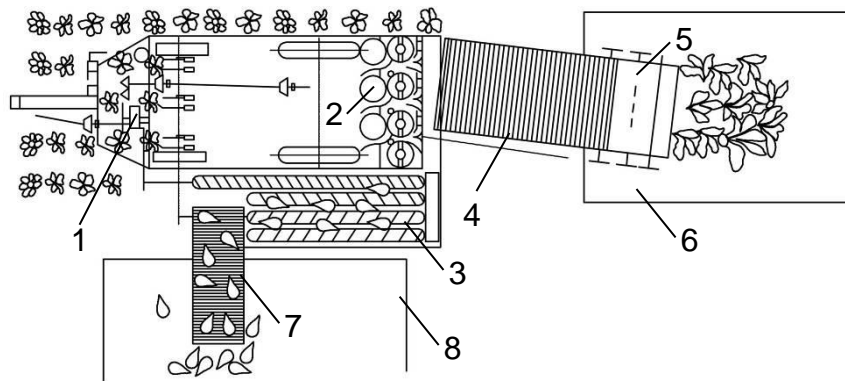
Конструктивно-технологічна схема коренезбиральної машини КСТ-3: 1 – гичкозрізувальний пристрій; 2 – дисковий вирівнювач-обрізник гички; 3 – шнековий очисник вороху; 4 – транспортер зрізаної гички; 5 – металевих гички; 6 – візок зрізаної гички; 7 – завантажувальний транспортер коренеплодів; 8 – транспортний засіб
